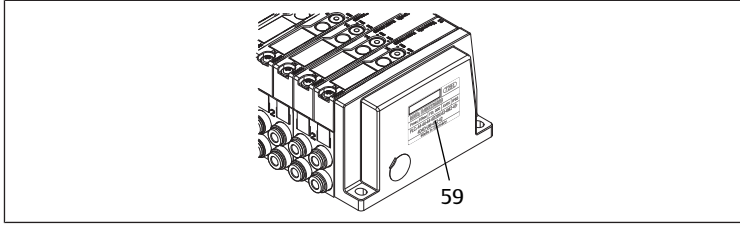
SPS-Konfigurationsschlüssel auf rechter Endplatte
